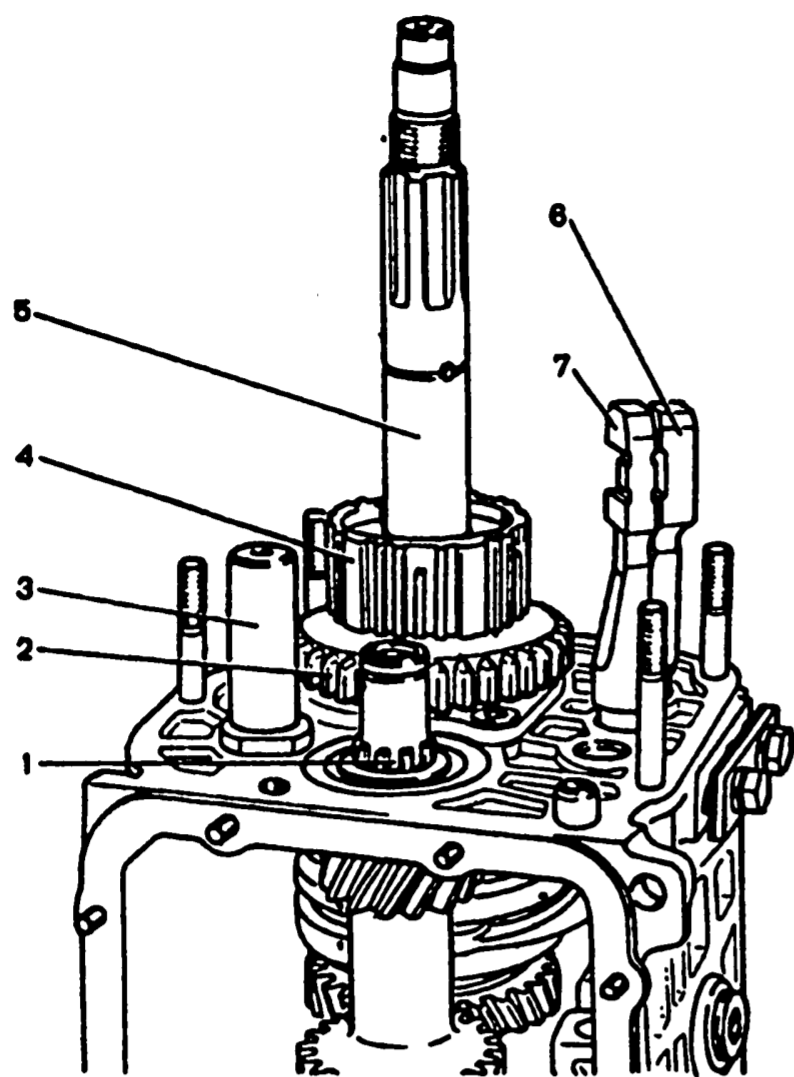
Снятие ведомой шестерни заднего хода и ступицы муфты синхронизатора V передачи: 1 - промежуточный вал; 2 - ведомая шестерня заднего хода; 3 - ось промежуточной шестерни заднего хода; 4 - ступица муфты синхронизатора V передачи; 5 - вторичный вал; 6 - шток вилки включения I и II передач; 7 - шток вилки включения III и IV передач
